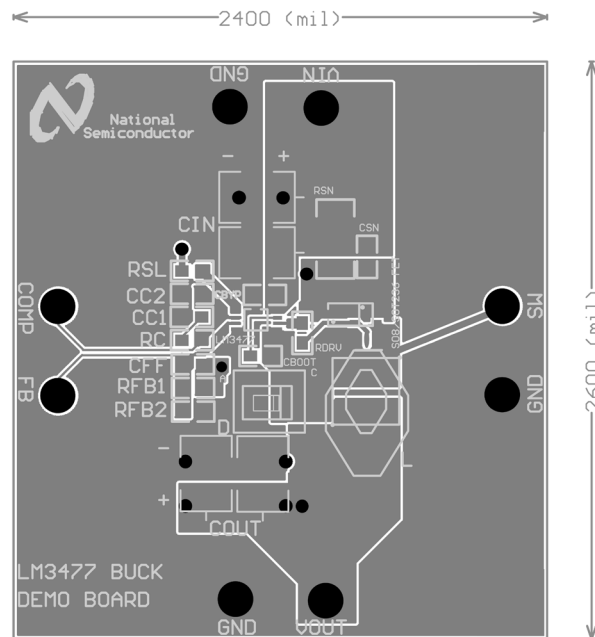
LM3477 评估板 PCB 布局 (顶面)
